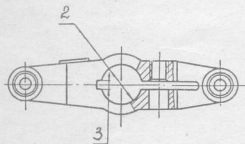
Передний фланец ведущей полумуфты привода ТНВД
